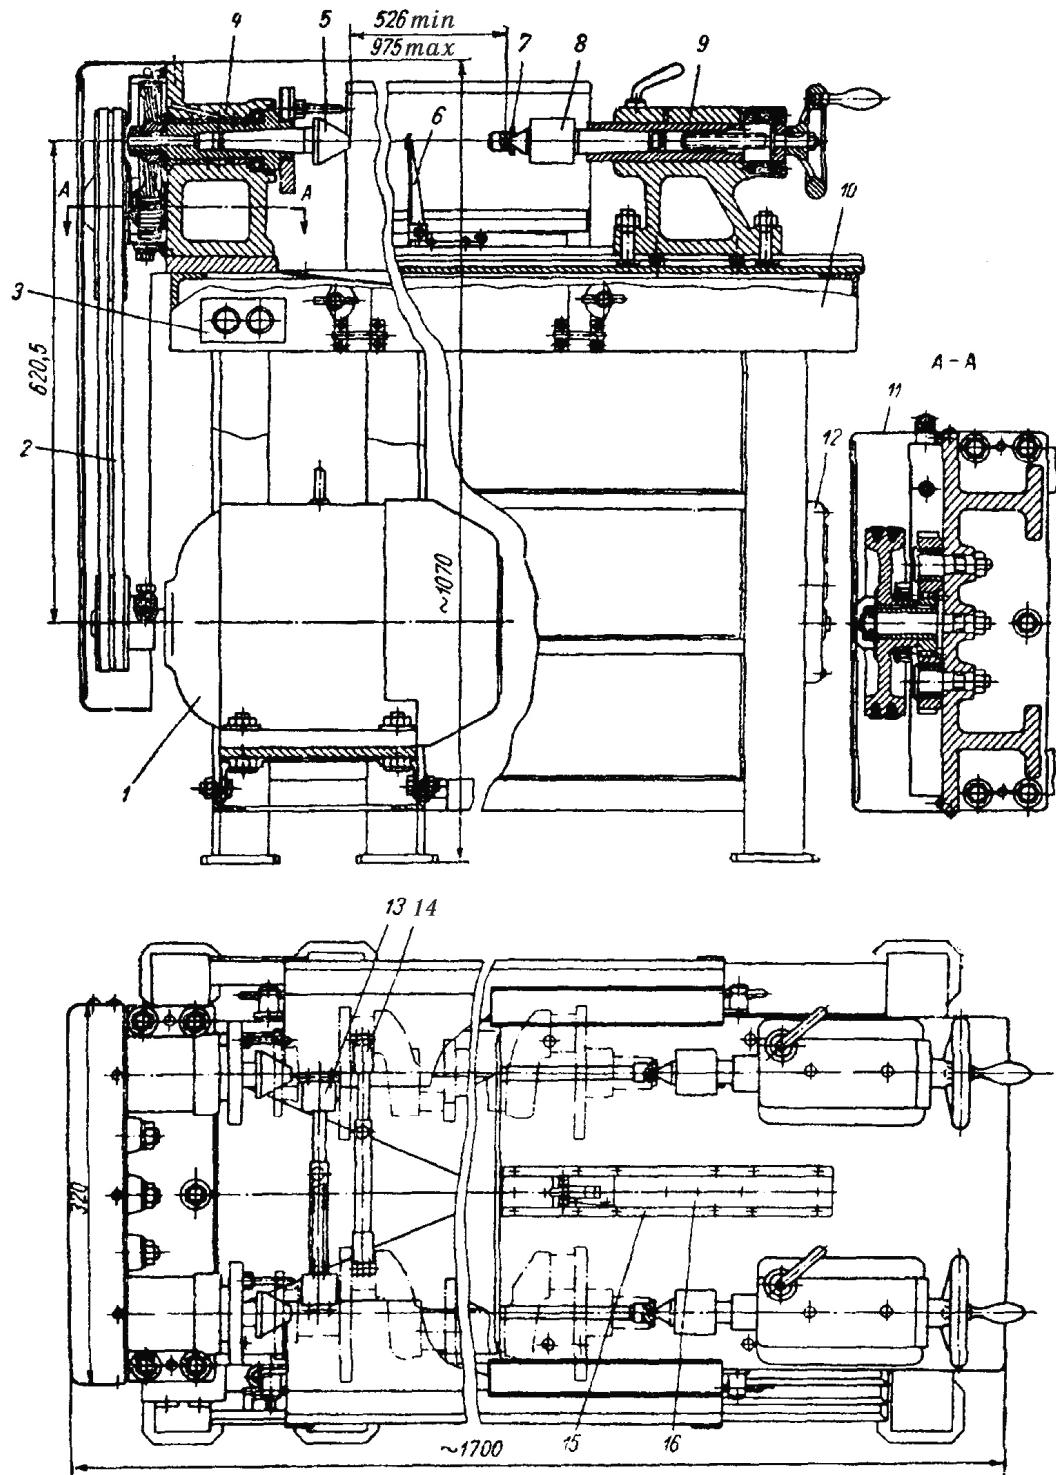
Верстат для полірування шийок колінчастих валів
